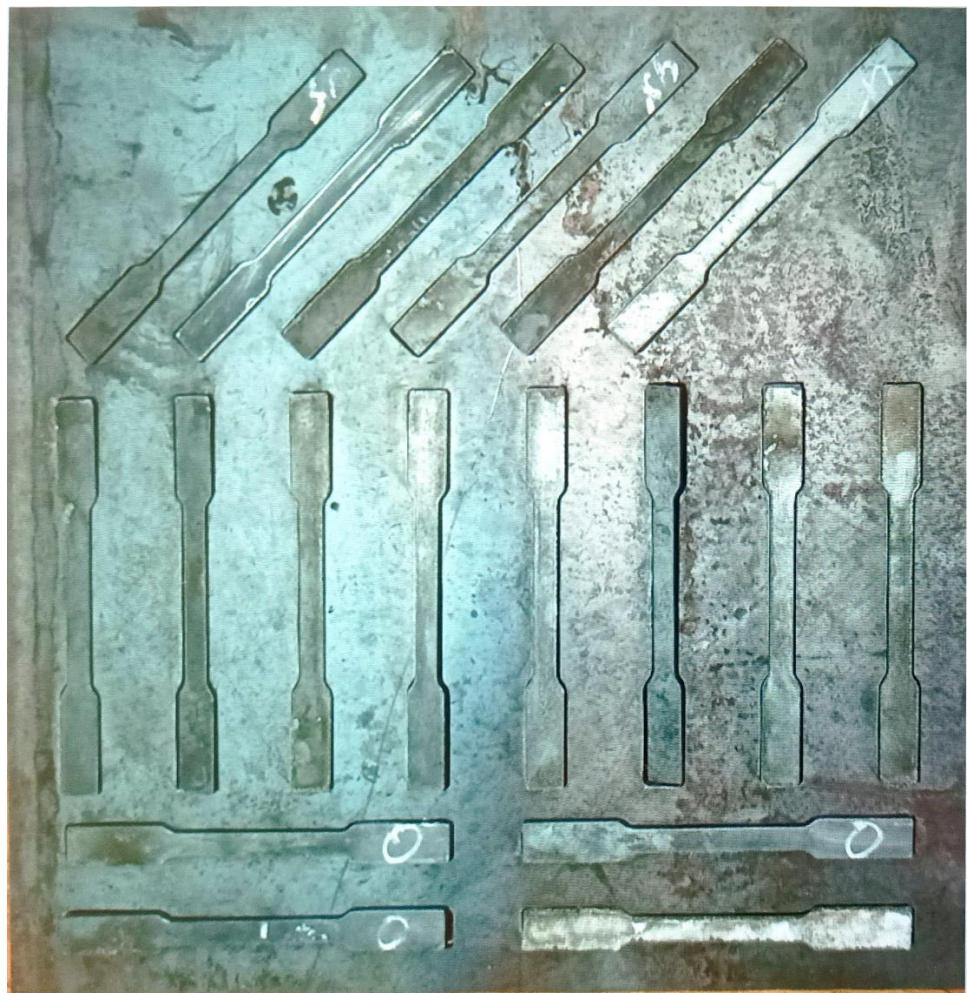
Eprouvettes découpées par CNC plasma à 0°, 90° et 45°.
